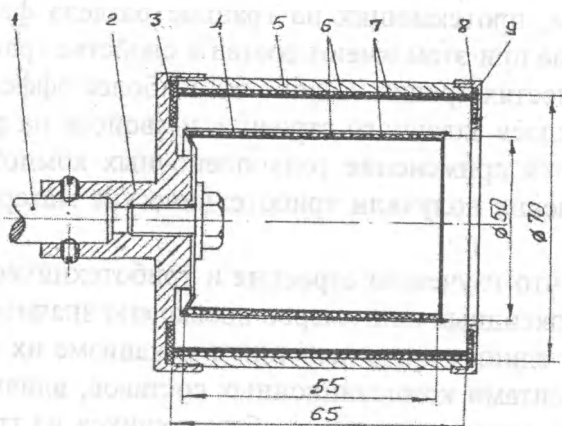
Устройство для получения пленок и покрытий центробежным способом: 1 – вал электропривода; 2 – крышка-днище; 3, 8 – прокладки уплотнительные антиадгезионные; 4 – цилиндр внутренний; 5 – корпус внешнего цилиндра; 6 – подложки технологические; 7 – формируемые покрытия; 9 – крышка внешняя
